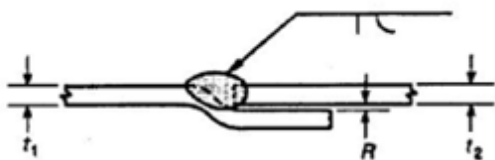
Soldadura de filete en junta de solape
